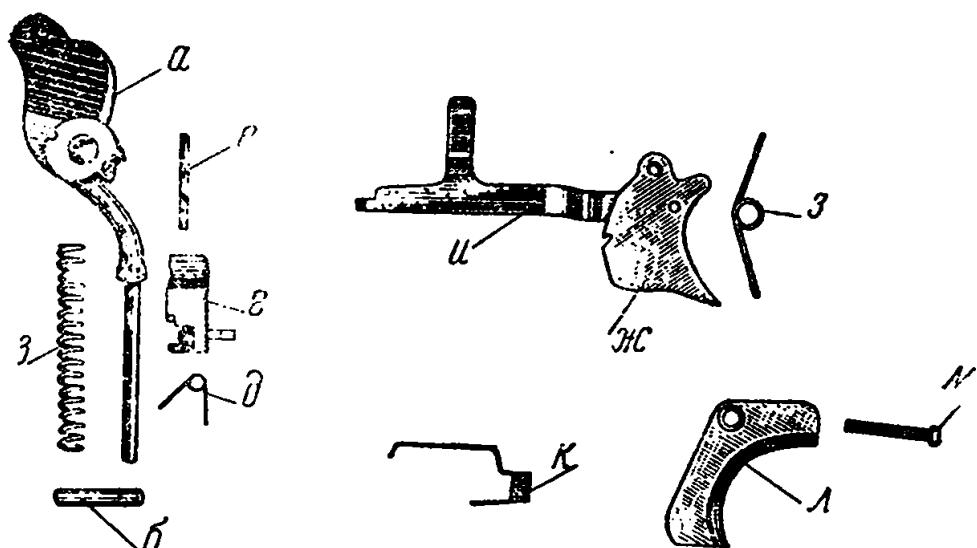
Ударно-спусковой механизм: а — курок с тягой; б — ось курка; в — боевая пружина; г — шептало; д — пружина шептала; е — ось шептала; жс — спусковой крючок; з — пружина спускового крючка; и — спусковая тяга; к — пружина спусковой тяги; л — щитик; м — винт щитика
